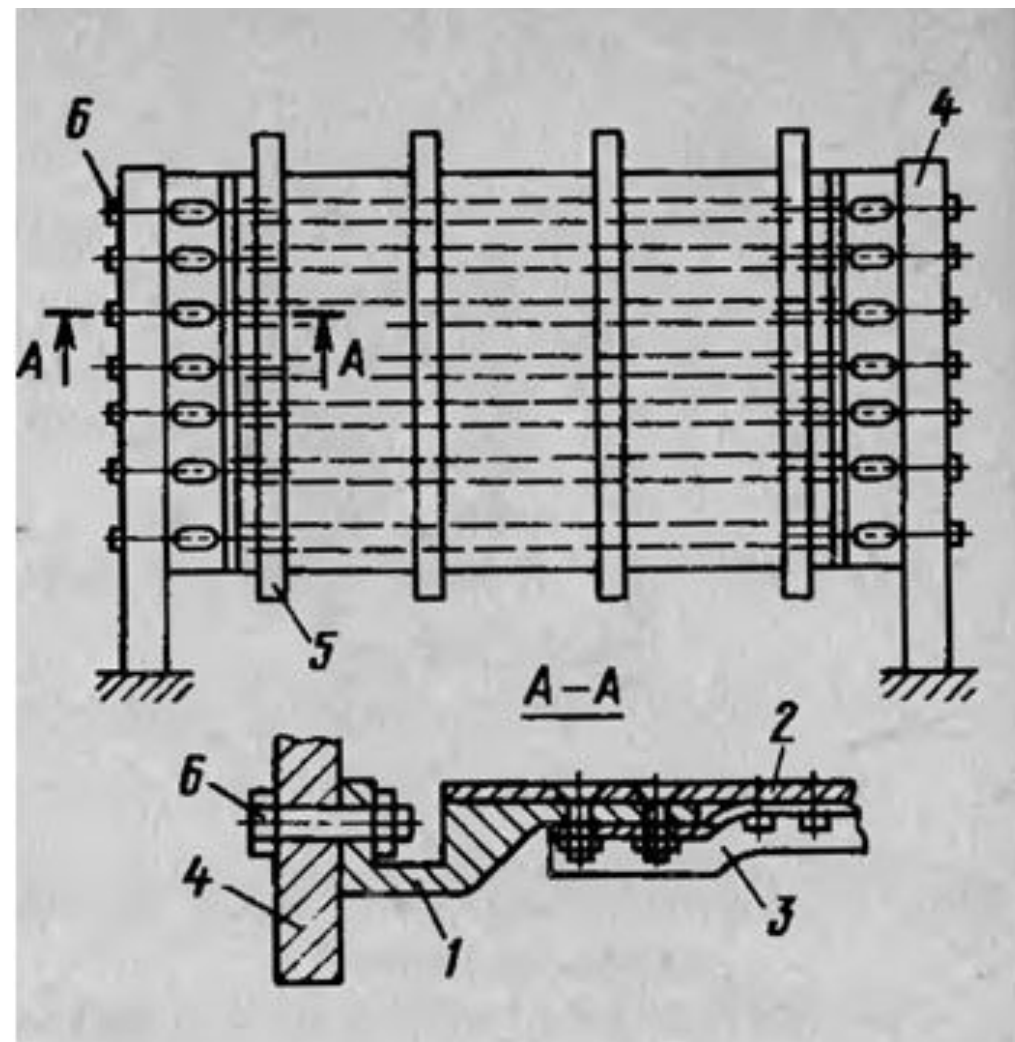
Схема сборки с базированием по отверстиям под стыковые болты:
